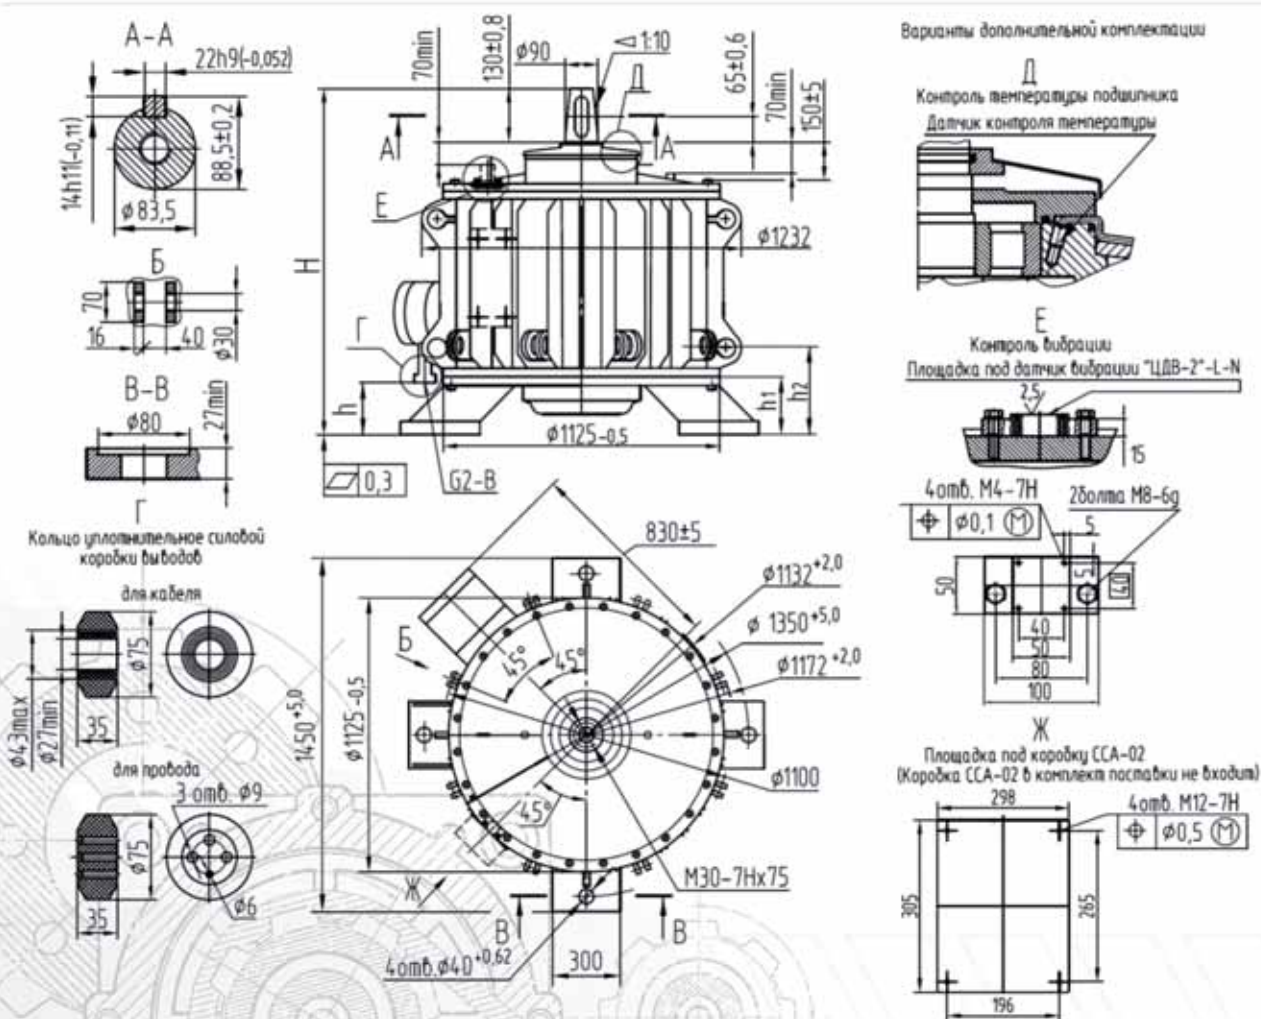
Габаритные и присоединительные размеры двигателей ВАСО5К
